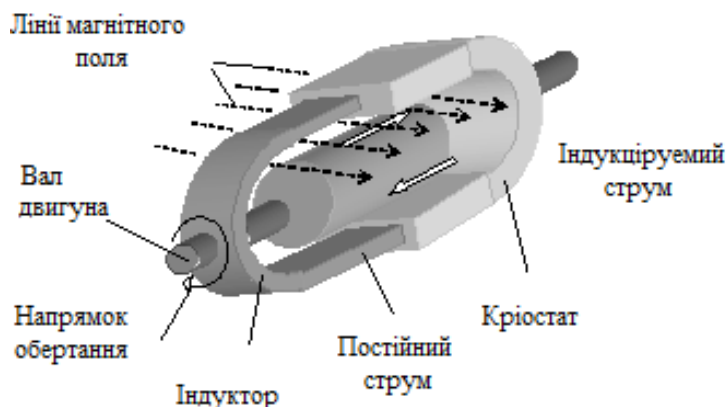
Індукційний нагрів заготовки в магнітному полі
